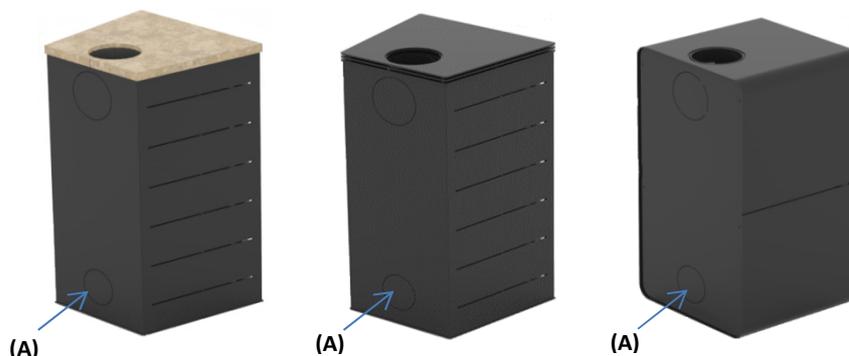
Vue arrière de chaque modèle ; (A) Section à extraire pour l'entrée d'air extérieure
